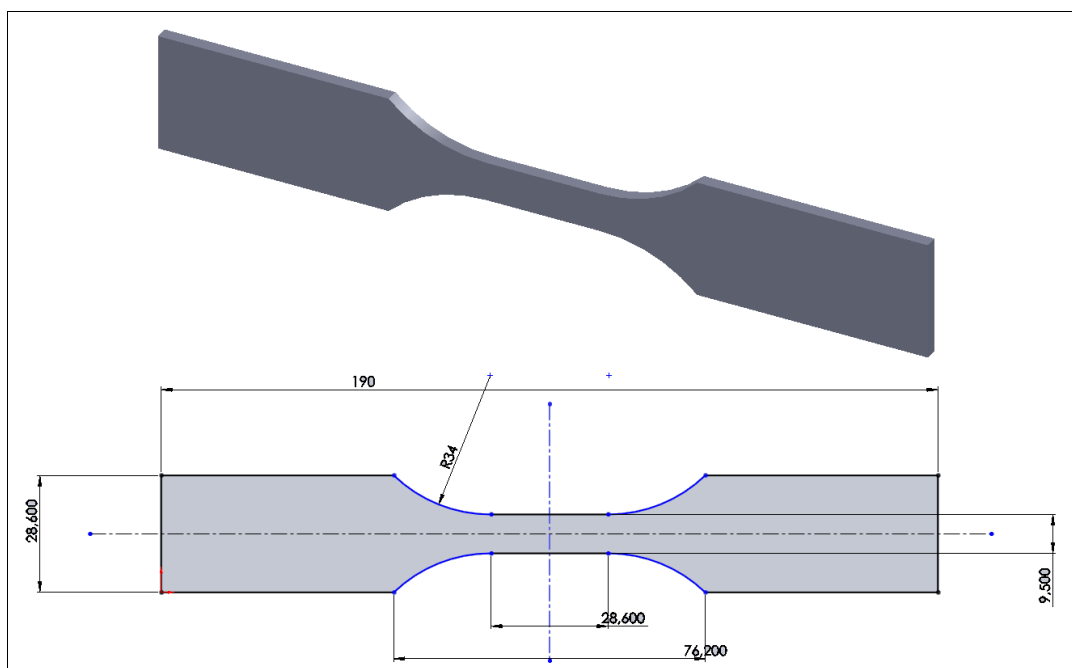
Dimensões dos Corpos de Prova segundo Norma ASTM D638-10.
